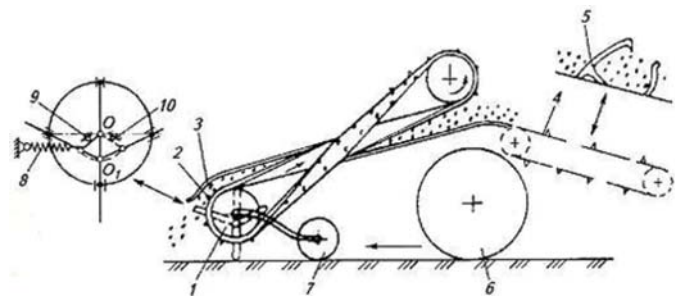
Конструкційна схема обертача стрічок льону: 1 - підбиральний барабан; 2 - обертальний перехресний стрічковий транспортер із зубами; 3 - напрямні гвинтоподібні прутки; 4 - розстиляльний транспортер; 5 - в'язальний апарат; 6- колісна ходова частина; 7 - копіювальне колесо 7; 8 – пружина; 9 і 10 упори
